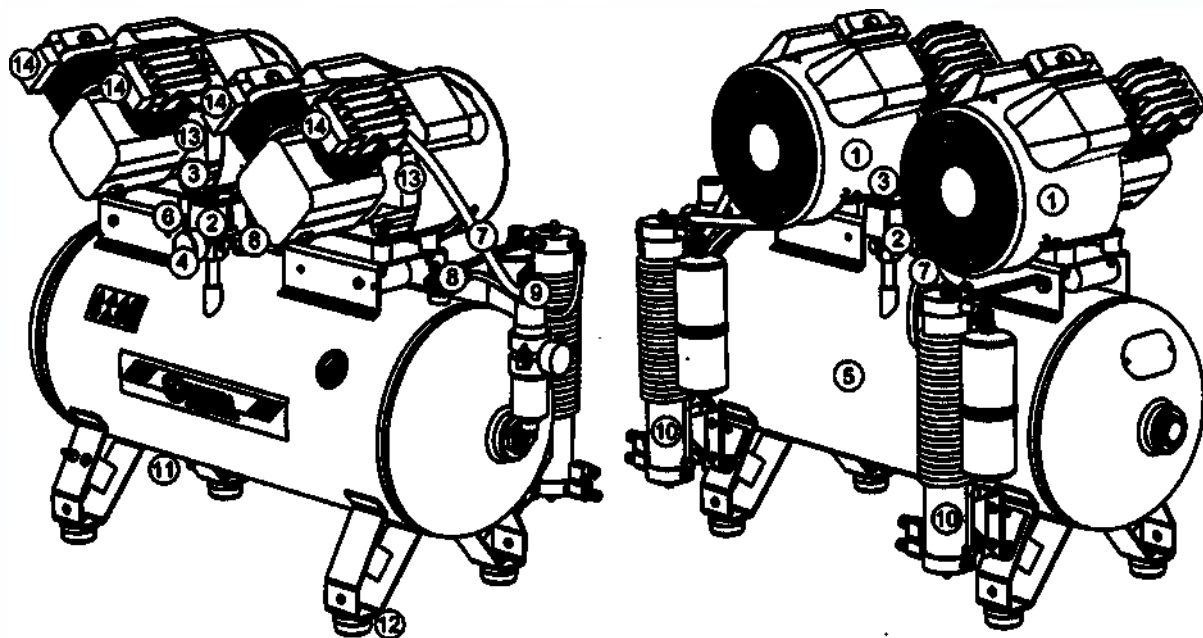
Общий вид компрессора KM-100.VS204ТД
